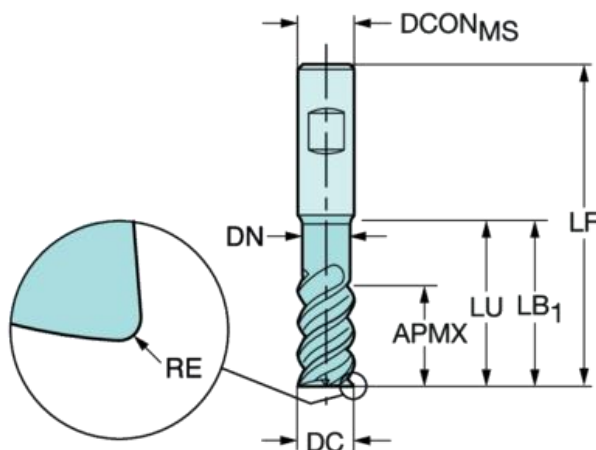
Кінцева Фреза 2P342-1600-РВ Р2ВМ
